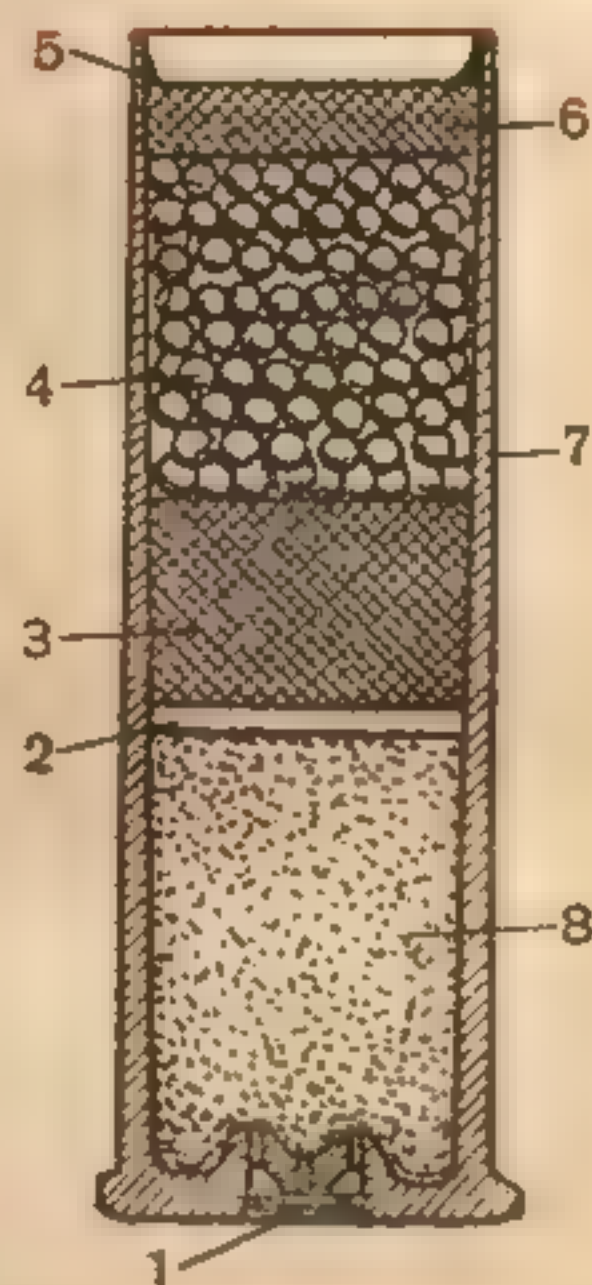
Дробовой патрон, снаряженный в металлическую гильзу
